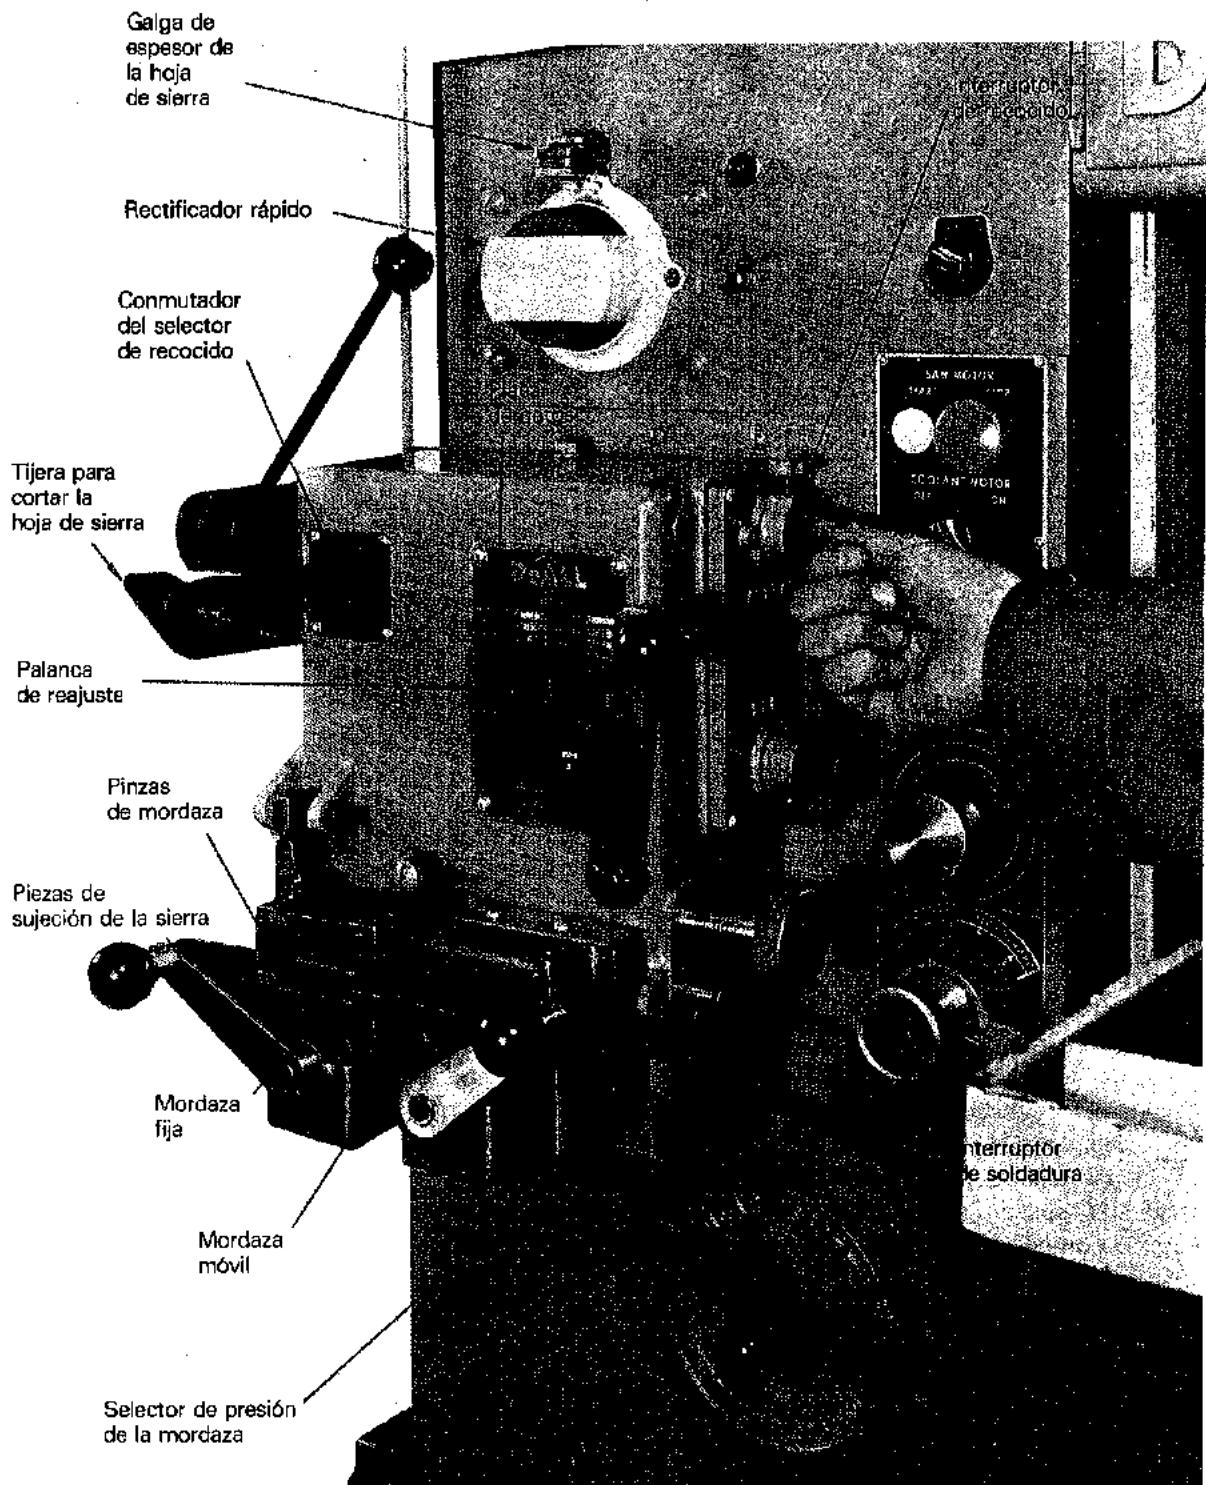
Unidad de corte-amolado-soldadura fijada a la columna de una máquina de sierra de cinta moderna (DoAll Co.)
